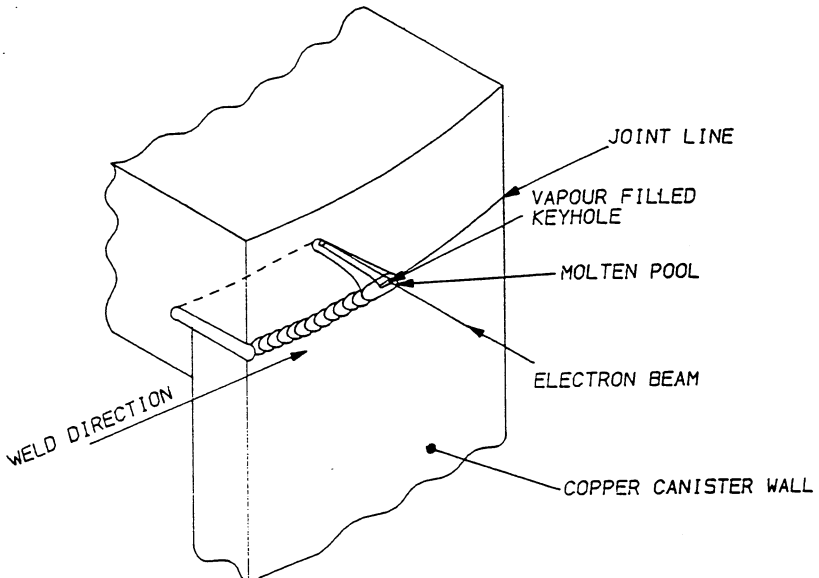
Svetsning med elektronstråle (ref. SKI-Report 95:6)
